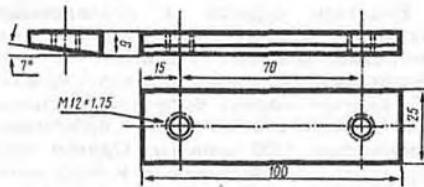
По этим размерам следует изготовить пластины для крепления задней опоры двигателя (если на внутренней поверхности фланца картера сцепления нет бобышек).
